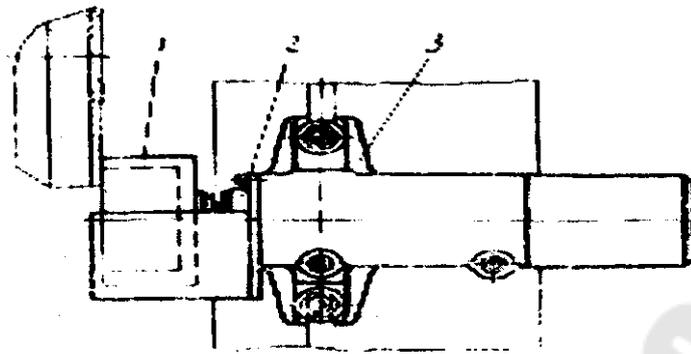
Приспособление для правки алмазного круга на полуавтомате мод. ЗЕ624
